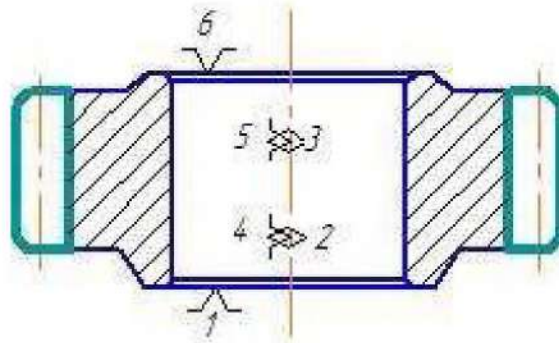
Схема базування заготовки на зубонарізній операції 025
